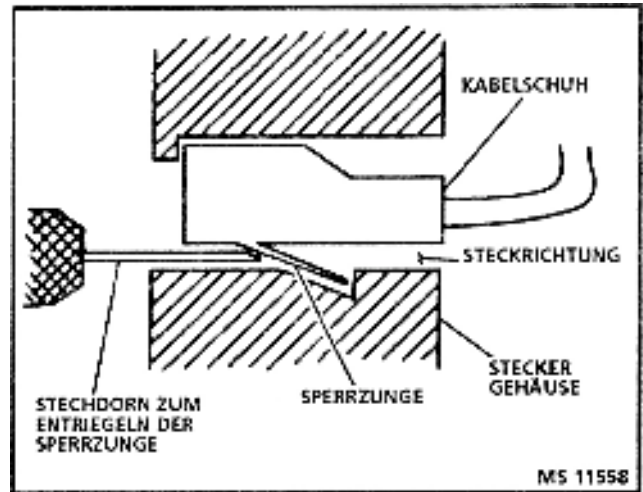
Typische Push-to-Seat Steckverbindung und Kabelschuh
